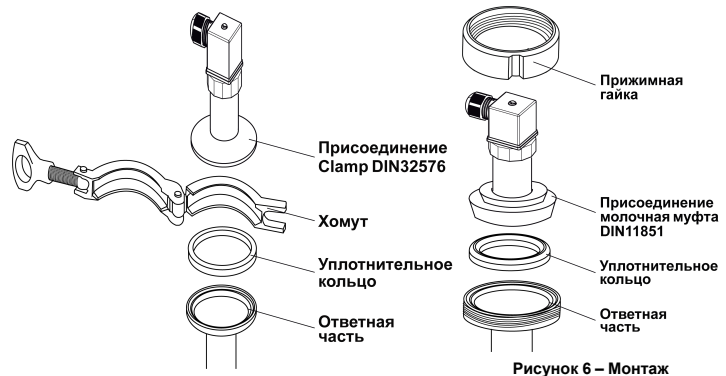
Монтаж с присоединением Clamp DIN 32576
